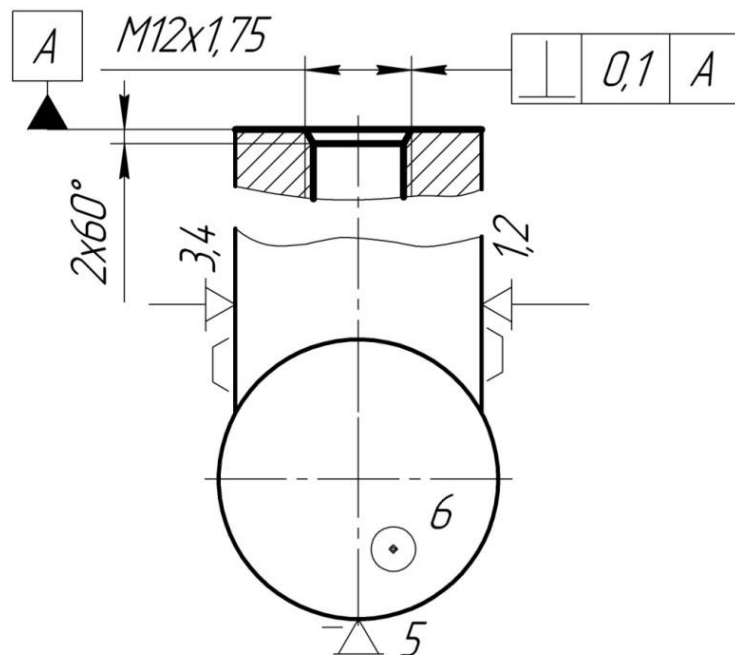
Схема базування заготовки на першому верстаті
